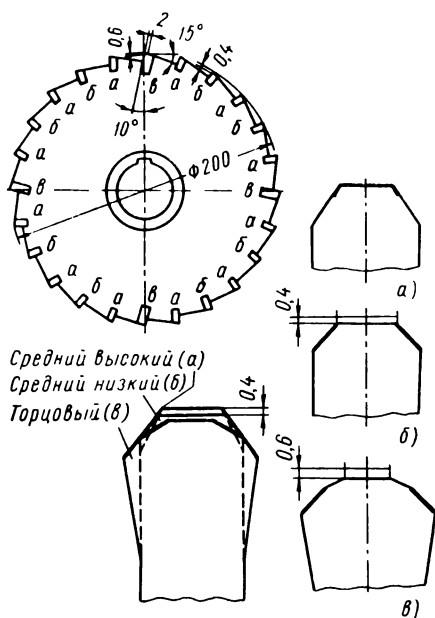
Прорезная сборная фреза для скоростного резания конструкции инж. Н. П. Чернова
